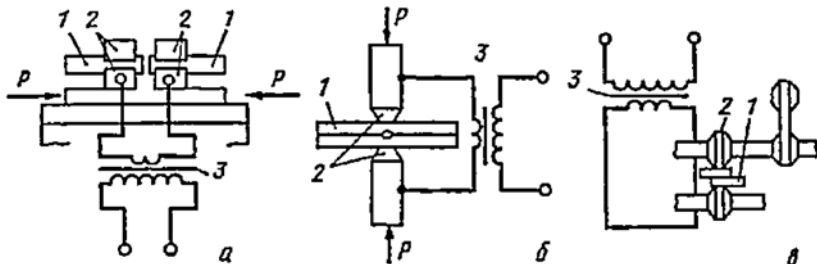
Виды контактной сварки: а – стыковая сварка, б – точечная сварка, в – шовная сварка; 1 – свариваемые детали, 2 – электроды-токопроводы; 3 – сварочный трансформатор.
